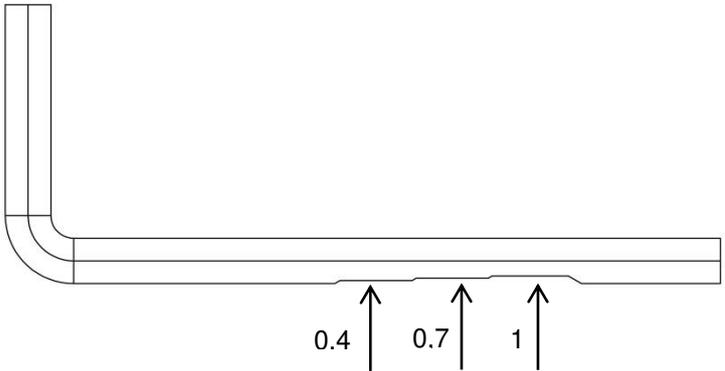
Innensechskantschlüssel mit Einkerbungen
